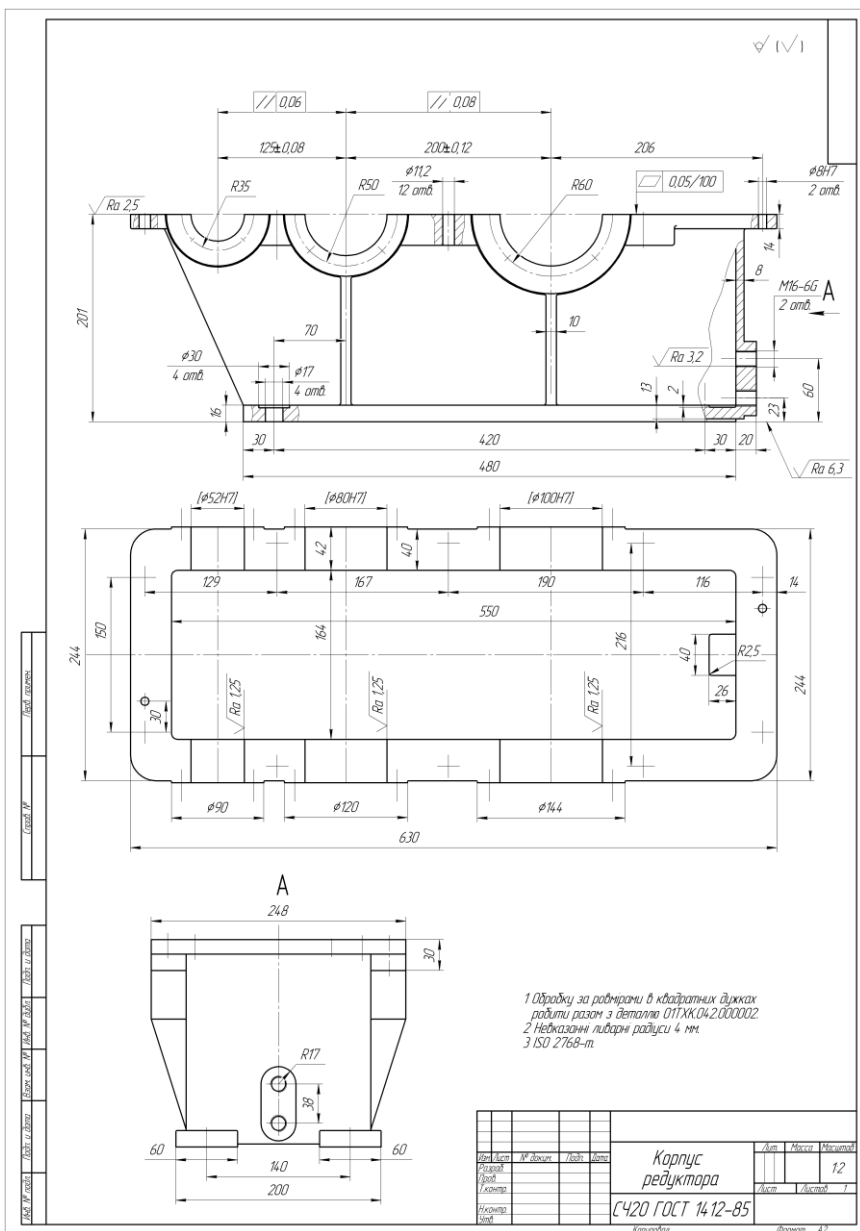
Приклад виконання робочого кресленника корпусу редуктора
